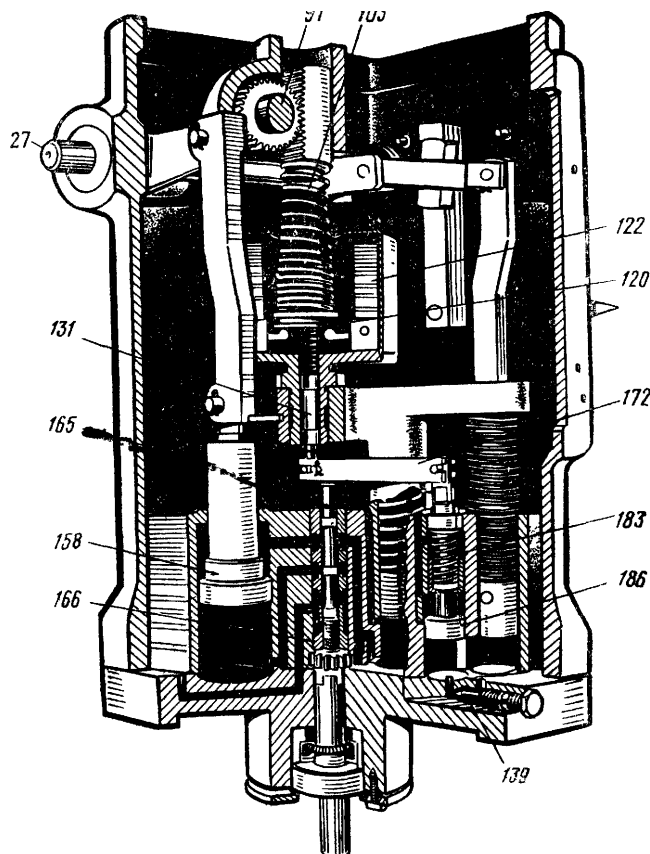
27—выходной вал; 91—вал-шестерня установки частоты вращения; 103—задающая пружина; 120—муфта с подшипником; 122—грузы регулятора; 131 — шток; 139 — игла изодрома; 158 — поршень сервомотора; 165—распределительный золотник; 166— втулка распределительного золотника; 172—плавающий рычаг; 183 — пружина изодрома; 186 — принимающий поршень изодрома
